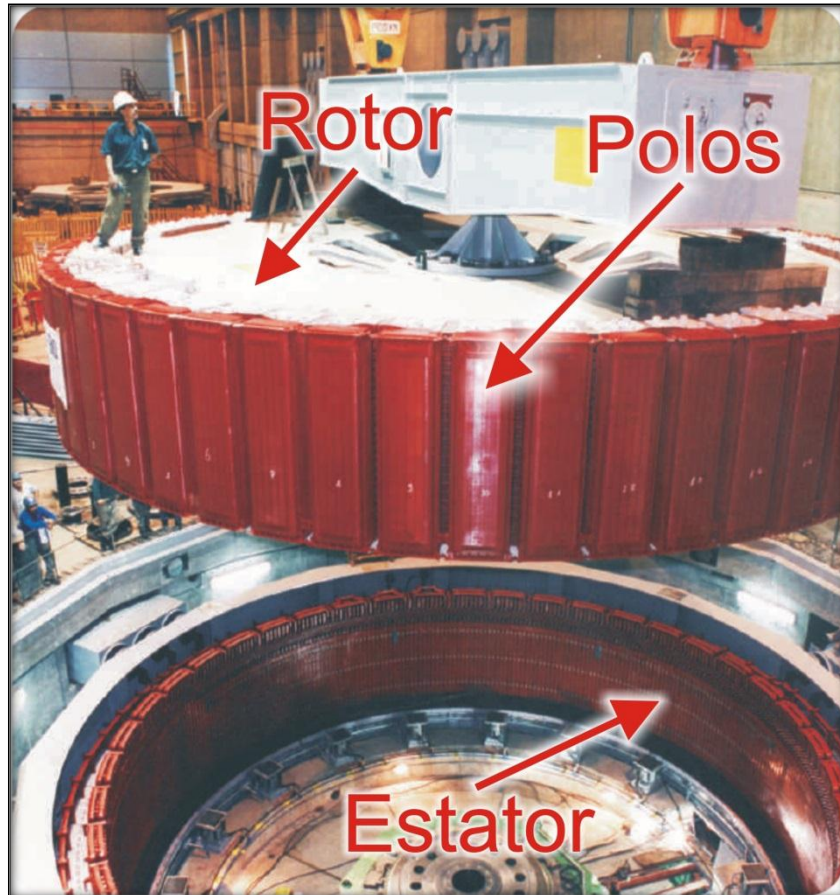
Rotor e Estator, adaptado de www.impsa.com
